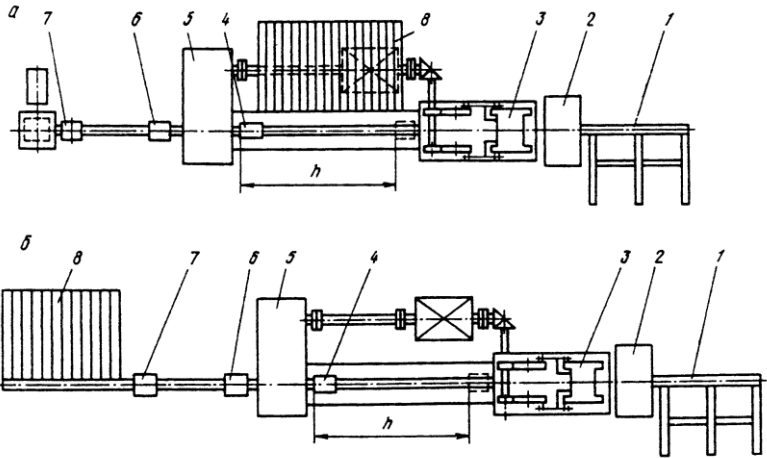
Схеми розташування устаткування станів холодної прокатки труб з бічним (а) і торцевим (б) завантаженням заготовок
